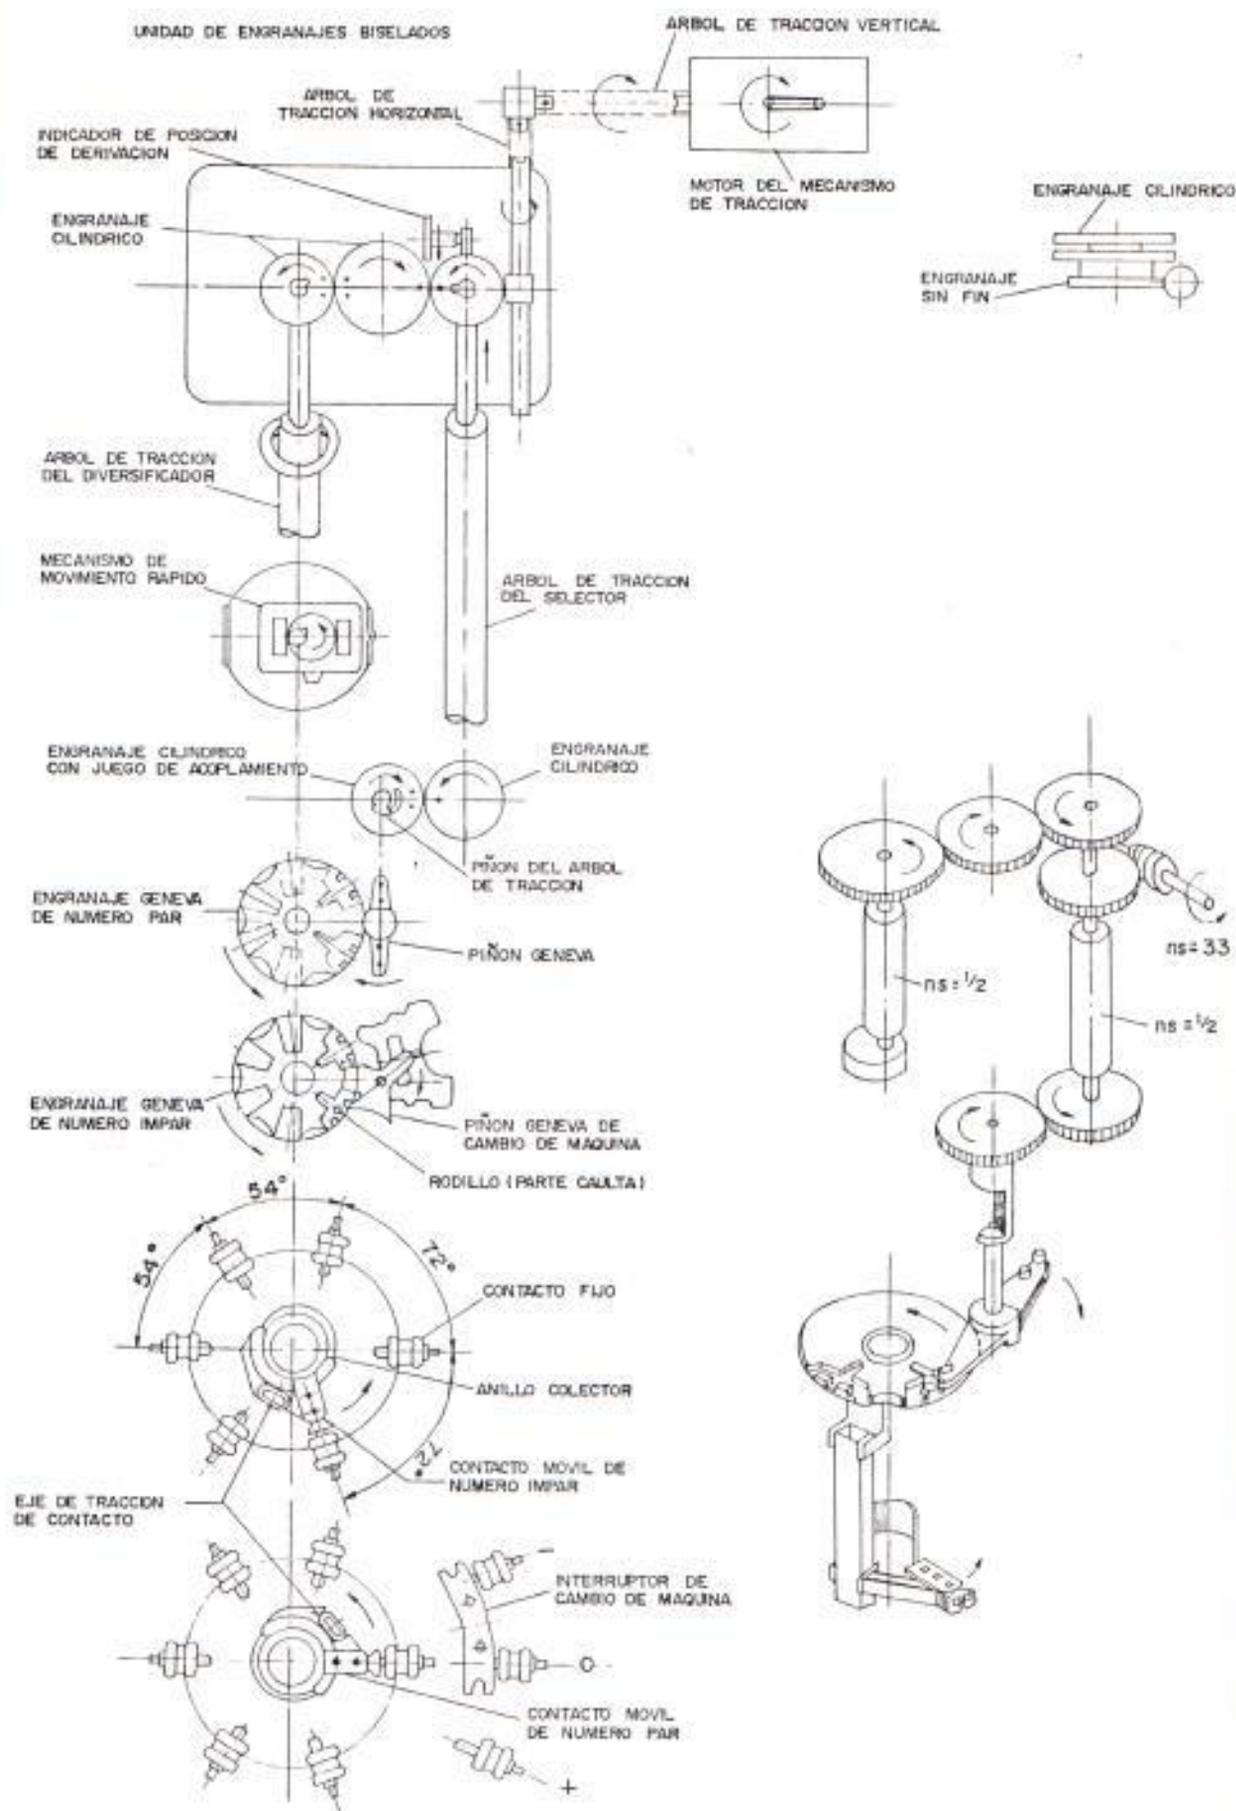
DISPOSICION DE LOS ENGRANAJES
